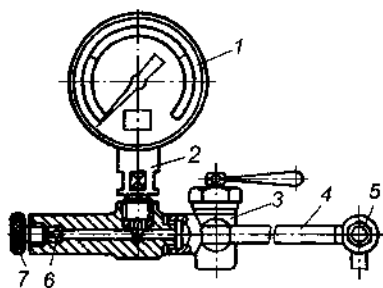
Устройство КИ-4801: 1 — манометр; 2 — корпус; 3 — трехходовой кран; 4 — шланг; 5 — пустотелый болт (штуцер); 6 — клапан; 7 — винт
